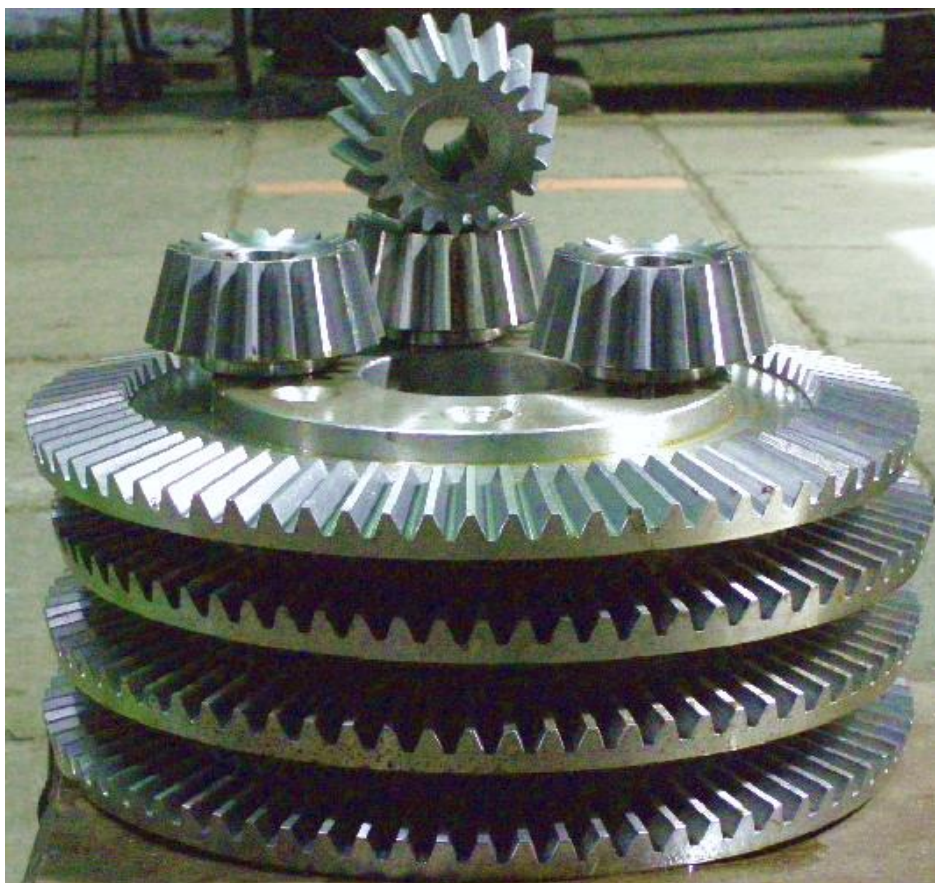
Готовые зубчатые венцы, обработанные на зуборезных станках
